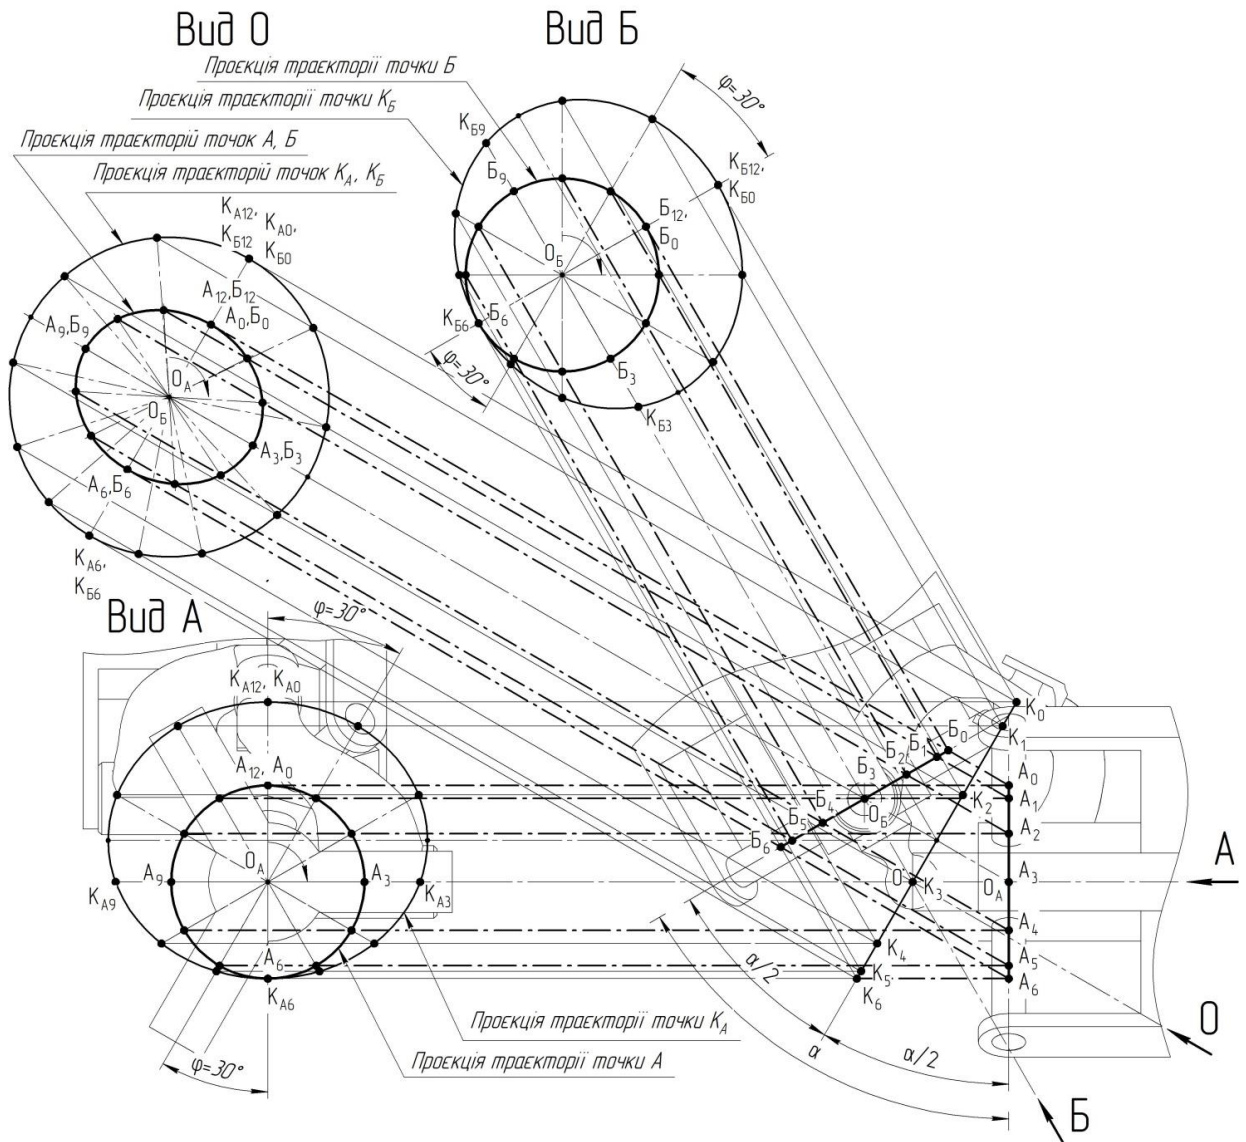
Розрахункова схема обраної конструкції шарнірного з'єднання
